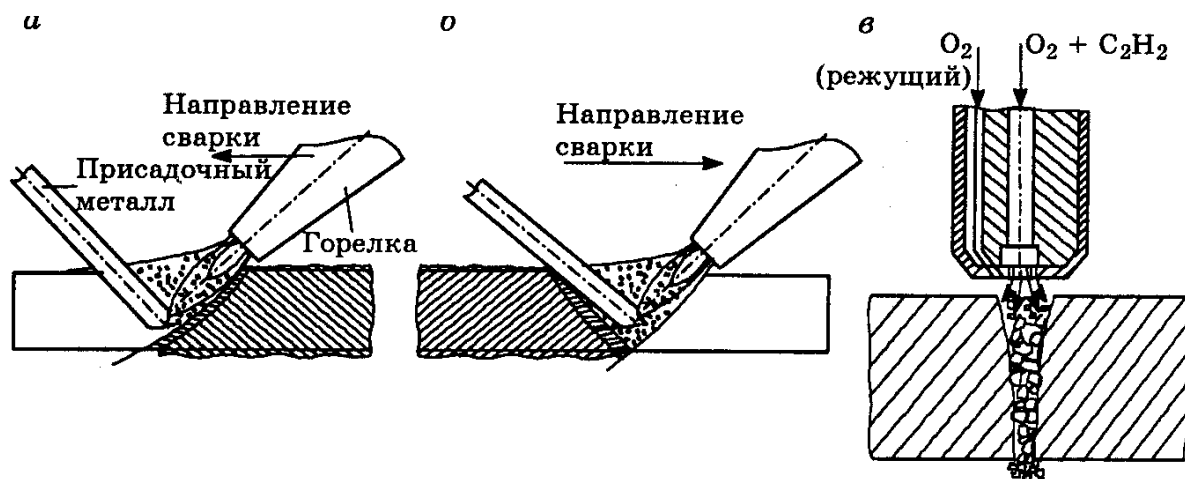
Способы газовой сварки (а — левый, б — правый) и резки (в)
